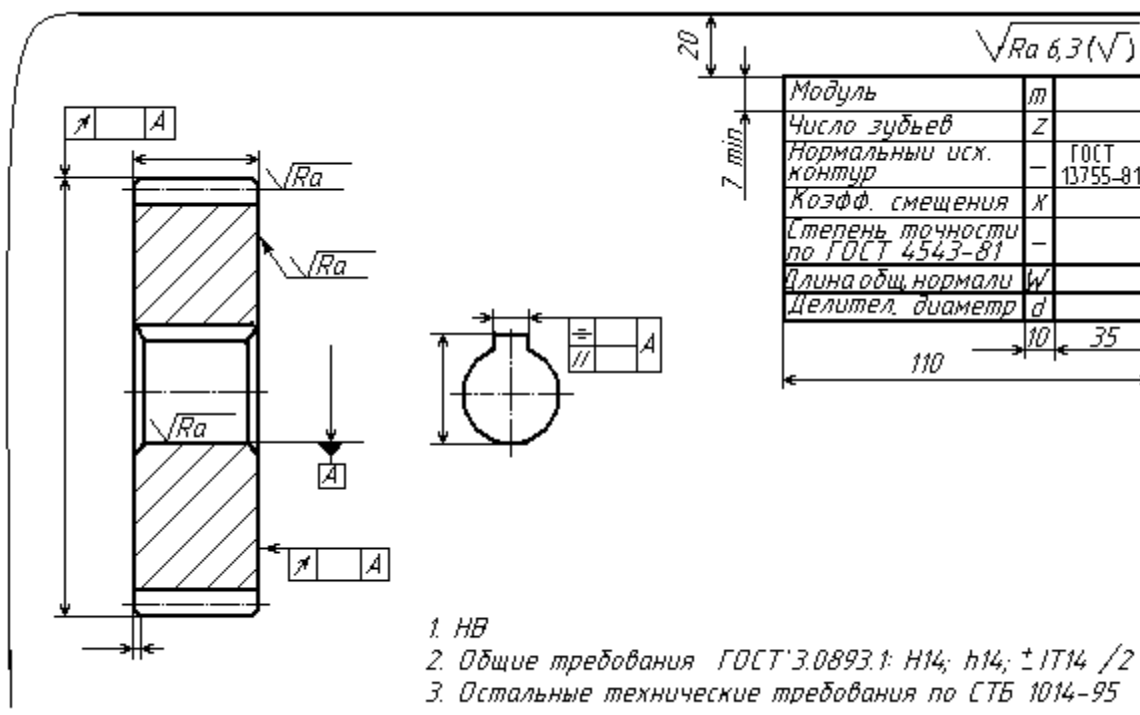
Пример оформления чертежа цилиндрического зубчатого колеса
